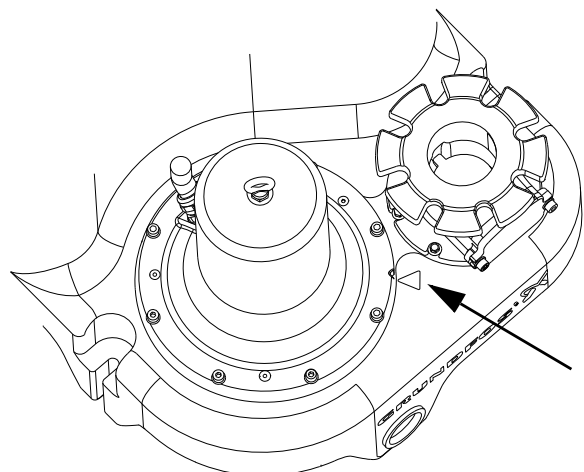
Метки совмещения на резервуаре и фланце насоса
